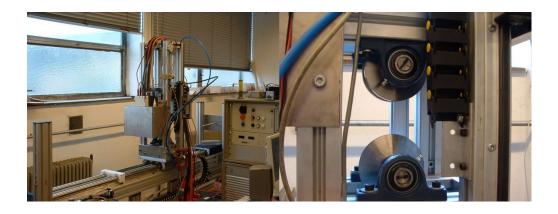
Device for laser assisted roll profiling of sheet metals.
